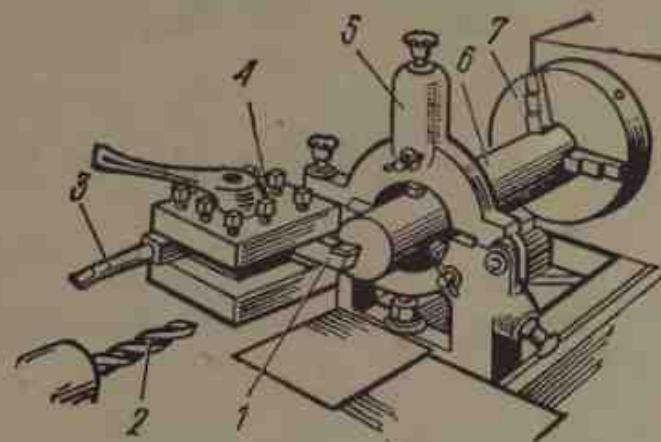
Установка и обработка длинной заготовки в патроне и люнете:
